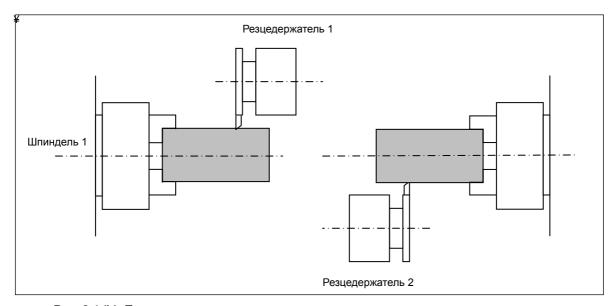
(b) Пример использования на токарном станке с двумя шпинделями и двумя резцедержателями
